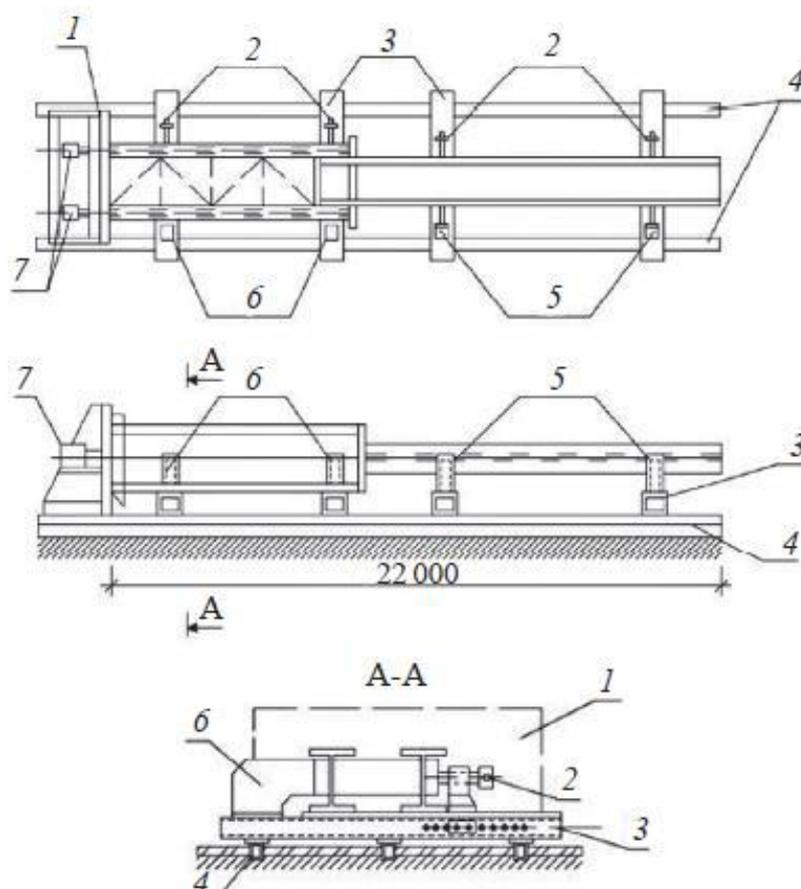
Способ сборки и сварки колонны строительной в сборочном кондукторе
